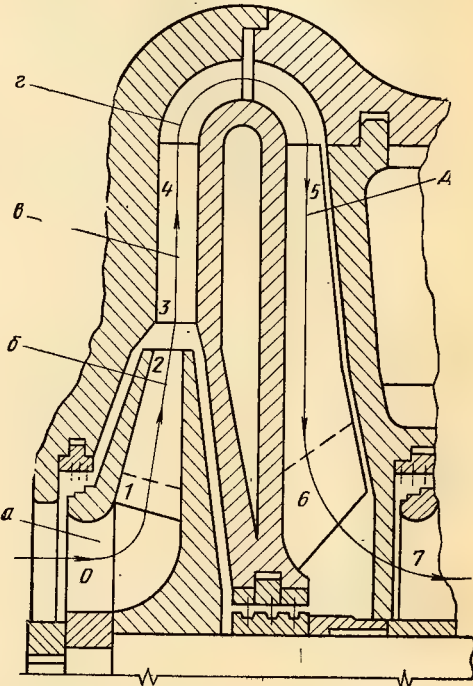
Схематическое изображение конструкции ступени многоступенчатого центробежного компрессора
